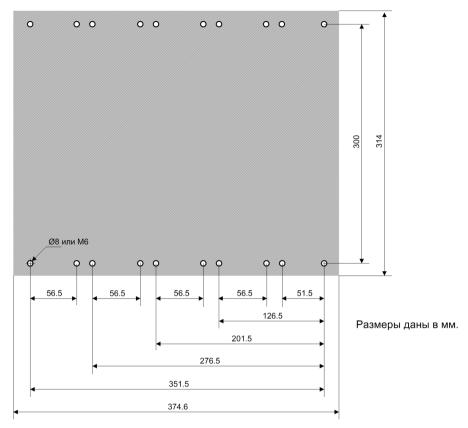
Схема сверления отверстий для устройства навесного монтажа 1/2, второй ряд устройств
